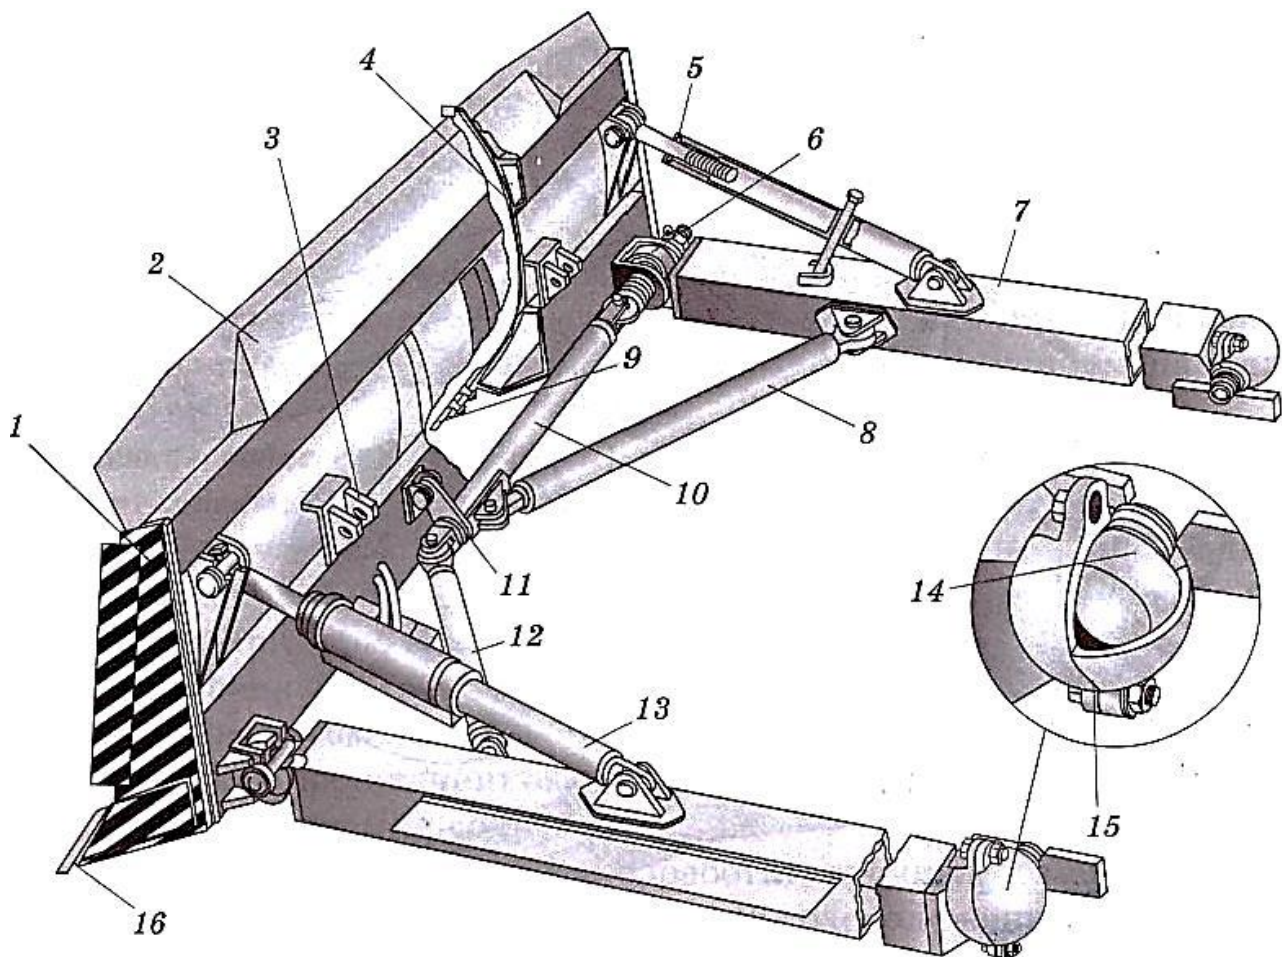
Оборудование бульдозера с неповоротным отвалом с шарнирным креплением:
